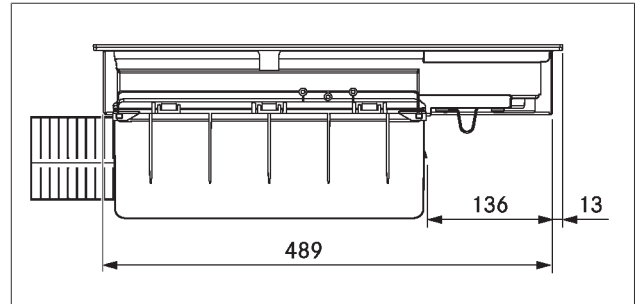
CKA2/CKA2AB apparatmått bild från sidan
